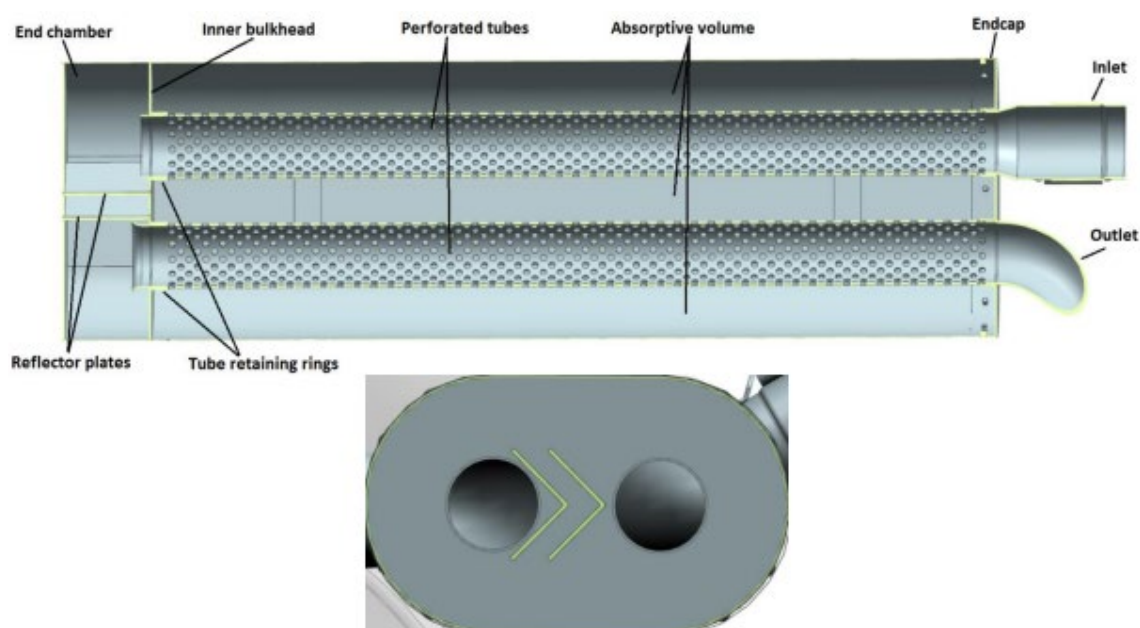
Внутренний конструктив глушителя команды Monash Motorsport
